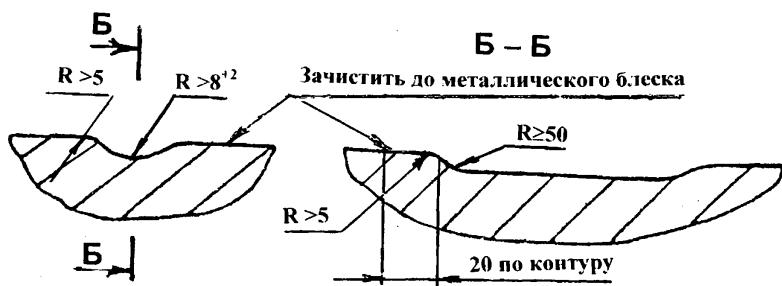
Выборка дефектов под заварку (наплавку) деталей из чугуна
